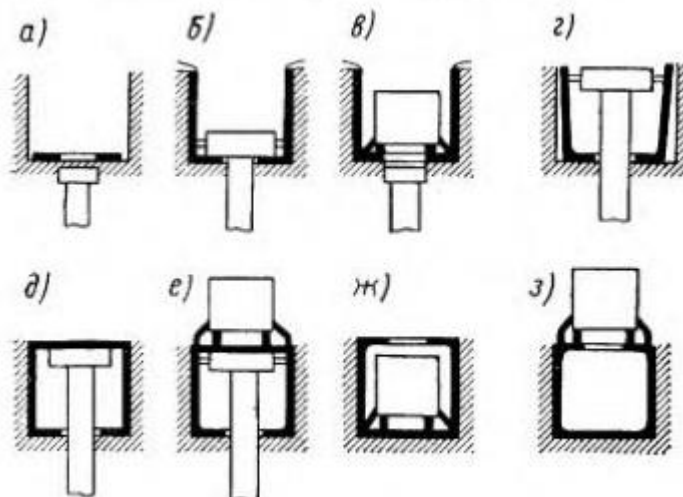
Последовательность сборочно-сварочных операций при изготовлении стержней коробчатого сечения
